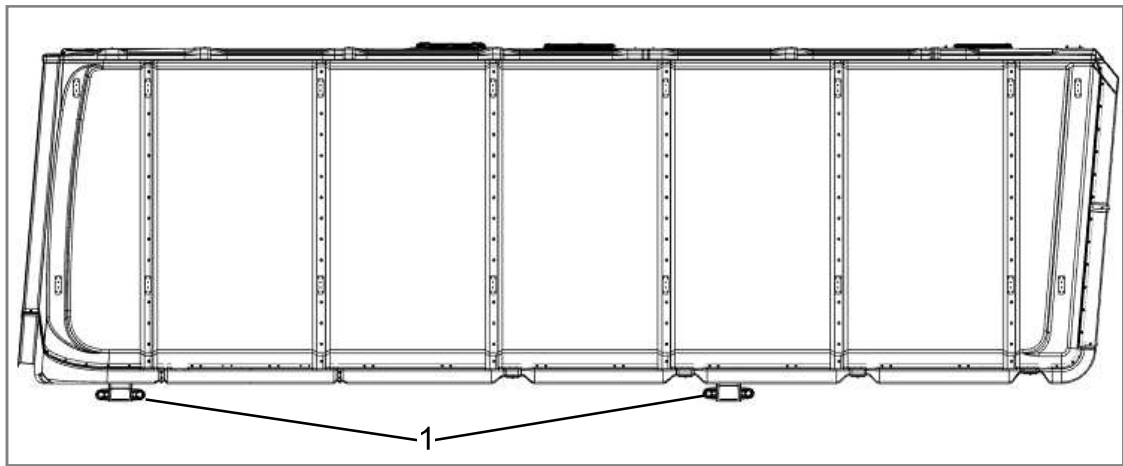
Beispieldarstellung Maschinenhaus, Ansicht seitlich mit Transportfüßen (1)
